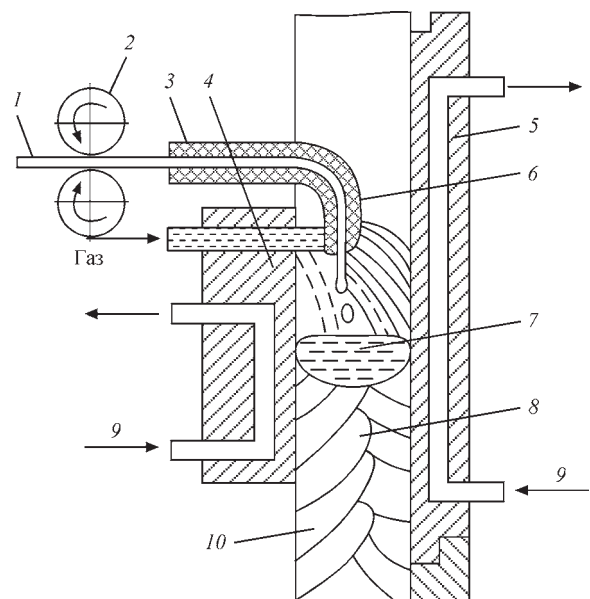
Схема зварювання плавким електродом у захисному газі вертикального шва з примусовим формуванням шва [37]: 1 – зварювальний дріт; 2 – механізм подачі дроту; 3 – струмопідвідний мундштук; 4, 5 – водоохолоджувані мідні повзуни; 6 – сопло; 7 – зварювальна ванна; 8 – зварний шов, що закристалізувався; 9 – вода; 10 – виріб
